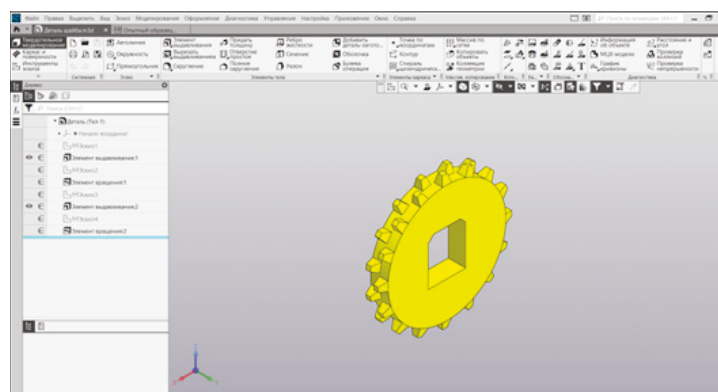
Опытный образец шайбы с ЗПП № 2 в 3D
